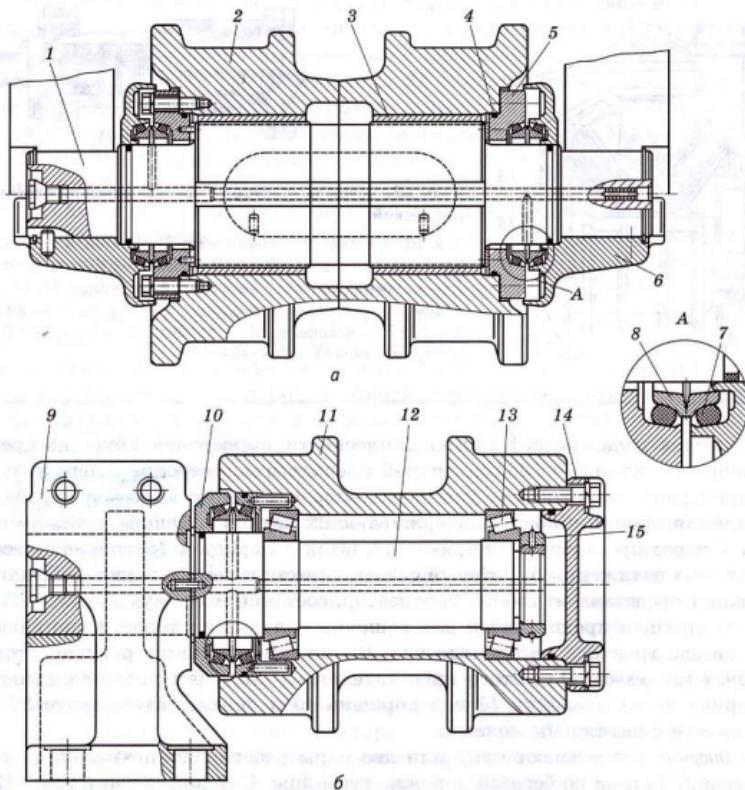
Опорный (а) и поддерживающий (б) катки:
